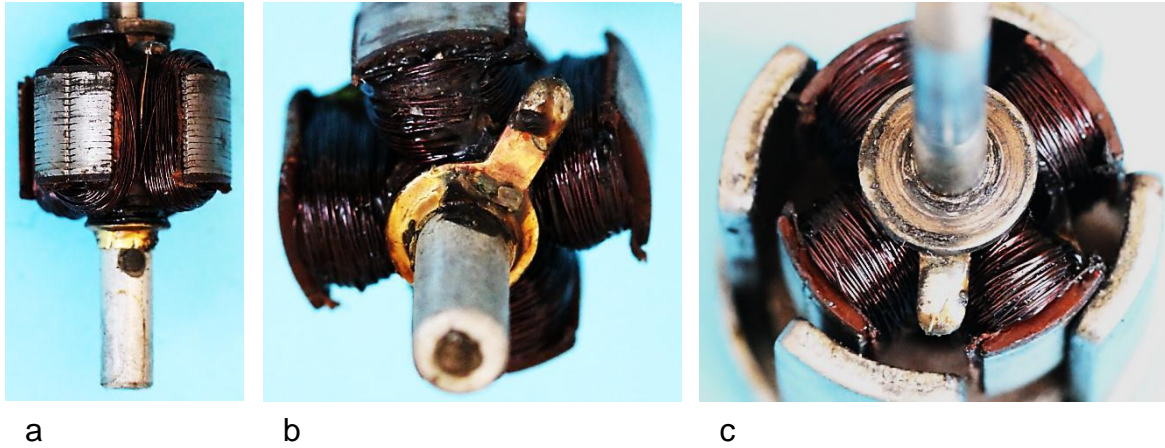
Wicklungsanschlüsse: a) Anker (Durchmesser 22 mm, Blechpaketlänge 11 mm, 16 Bleche), b) Spannung führender Kontakt, c) Schleifscheibe des Massekontakts
